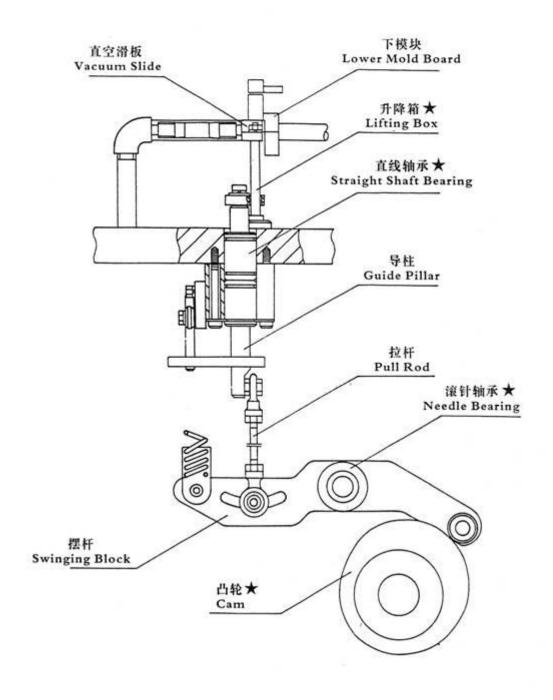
真空连接及传动机构 Figure 18 Vacuum Connection And Transmission Mechanism
